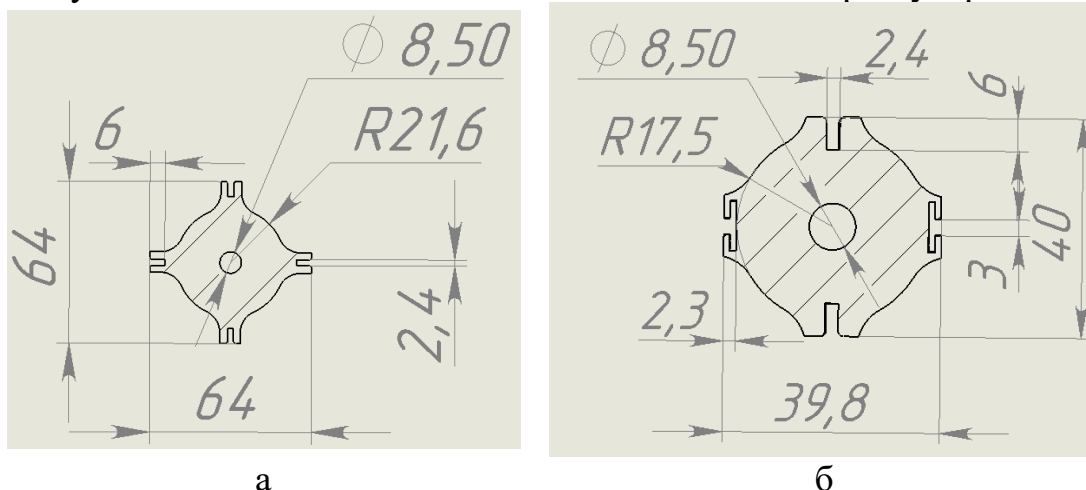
Форма корпуса вид сбоку; а – старая, б – новая
